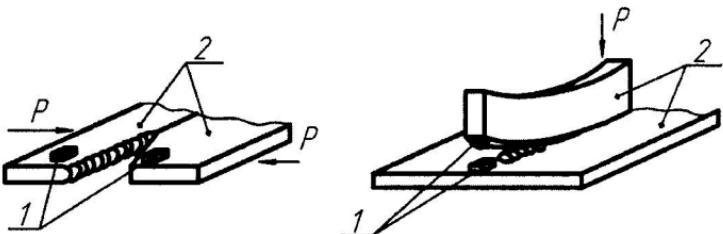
Приклади схем виконання високочастотного зварювання тиском з оплавленням: 1 – місця підведення струму; 2 – зварювані елементи
